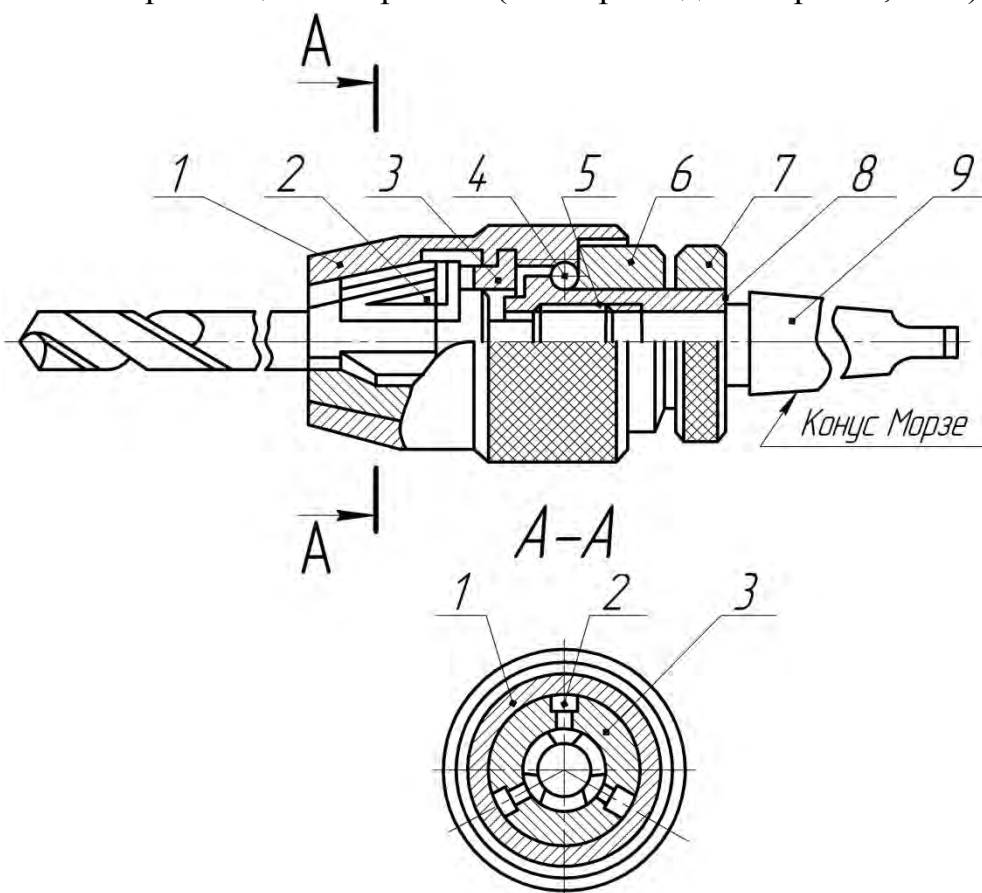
Трехкулачковый бесключевой сверлильный патрон
